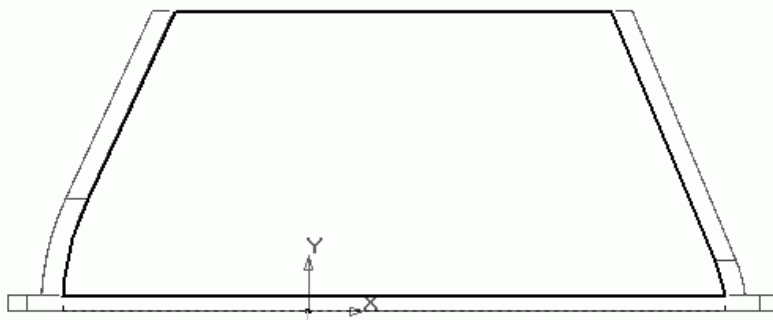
Эскиз для выдавливания боковой стенки корпуса редуктора
